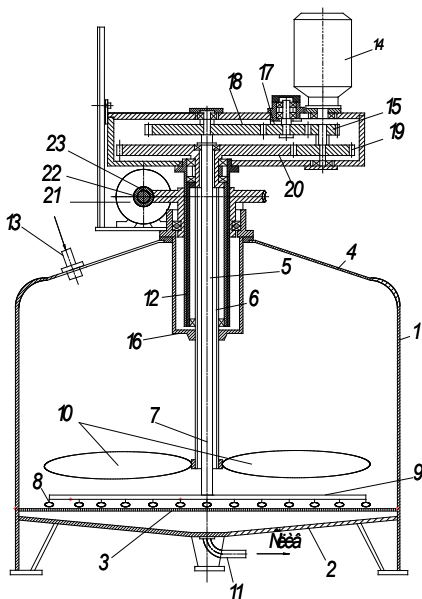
Устройство для фильтрации пивного сусла: 1 - корпус, 2 - днище, 3 - фильтрационная сетка, 4 - крышка, 5 - рыхлительный механизм, 6 - полый вал, 7 - подвижная ось, 8 - поперечный держатель, 9 - ножи, 10 - пропеллер, 11, 12 - патрубки, 13 - входной люк для загрузки дробины, 14, 21 - мотор-редукторы, 15, 19 - ведущие шестерни, 16 - корпус, 17 - паразитная шестерня, 18, 20 - ведомая шестерня, 22 - червяк, 23 - червячное колесо.
